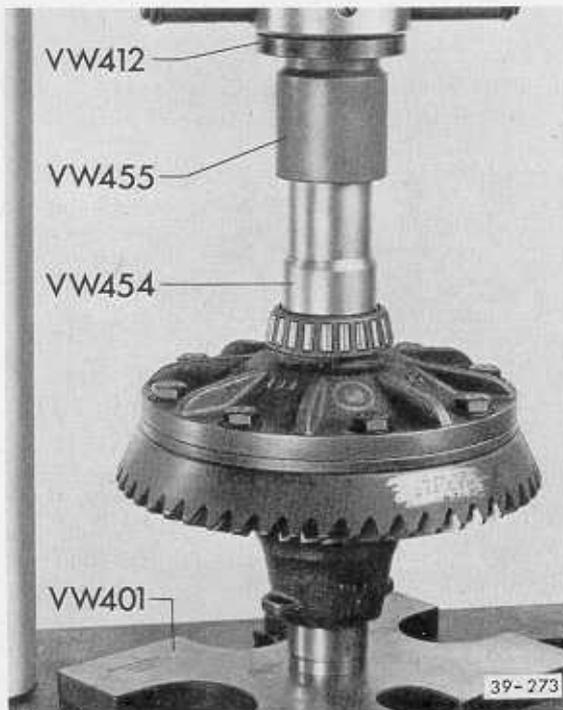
Kegelrollenlager auf ca. 100° C erwärmen,
